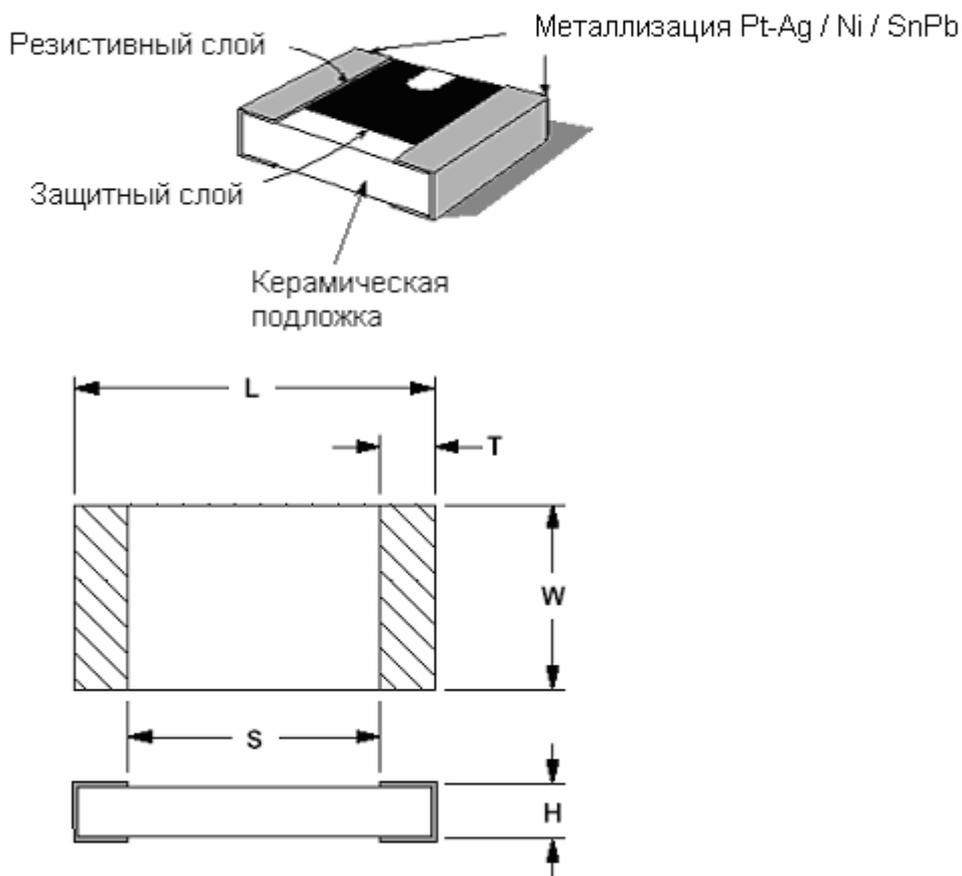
Безвыводной чип-резистор для поверхностного монтажа. Общий вид и габариты.
